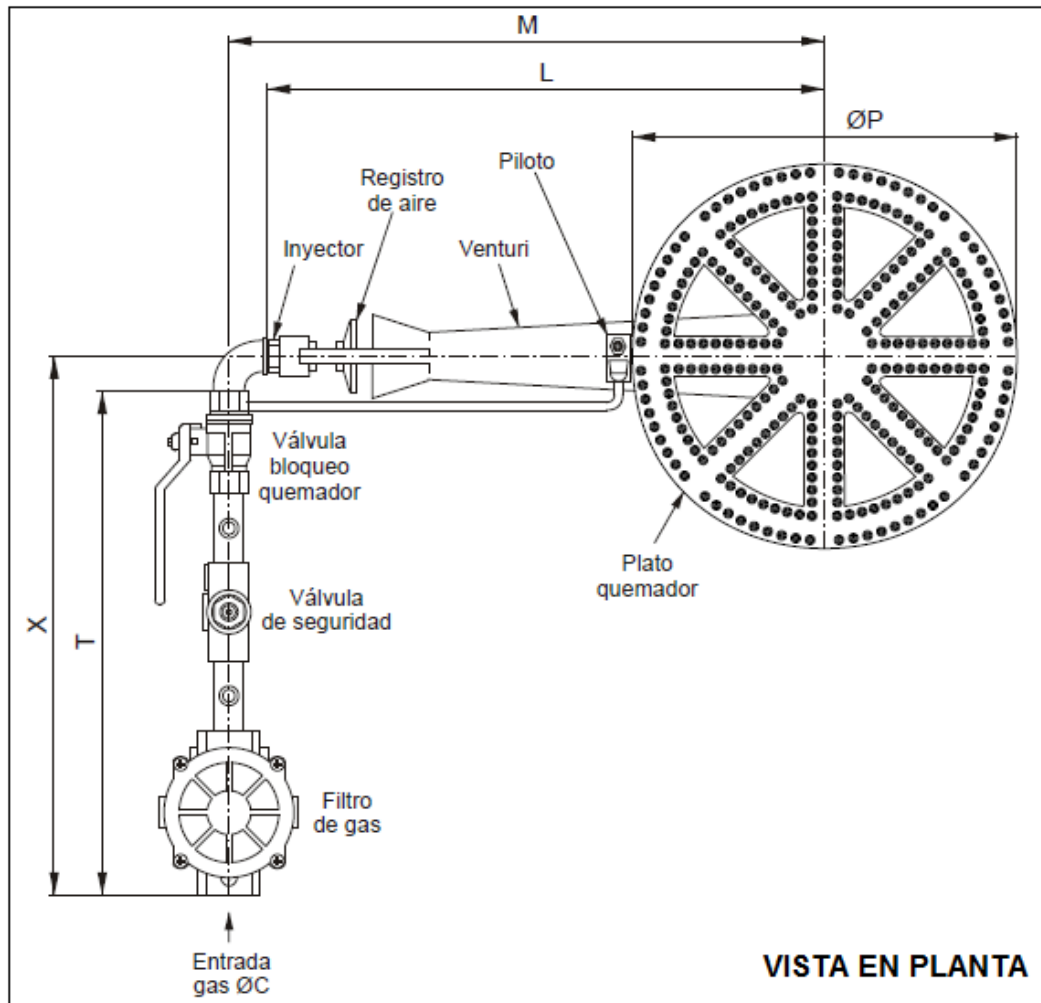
Vista en planta o superior del quemador de plato circular.
